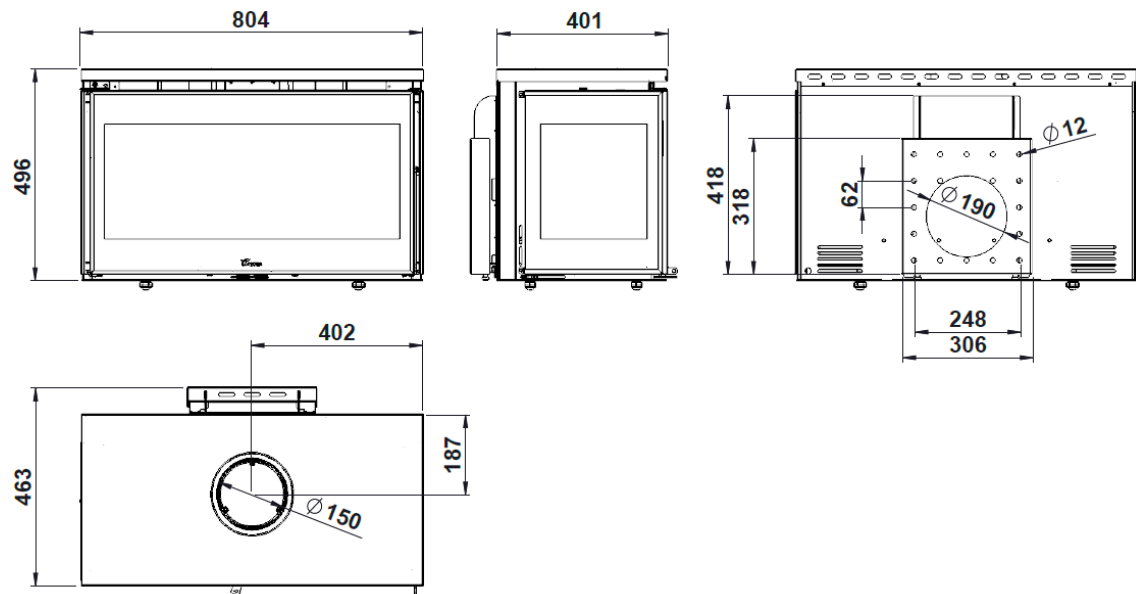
Dimensões em mm do aparelho PARIS 800 CLID MURAL
